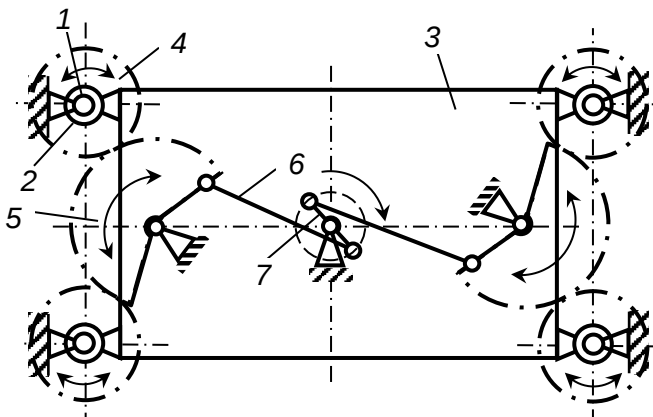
Схема штанцювального преса з використанням передачі гвинт-гайка
